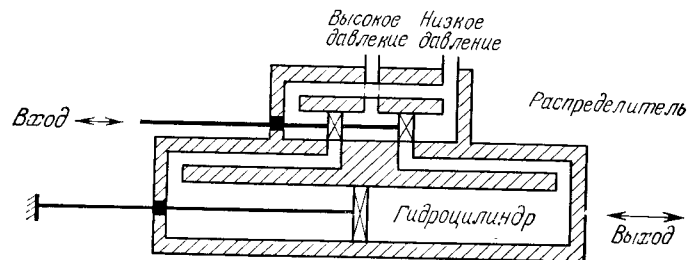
Следящий гидроцилиндр для поступательного движения.
